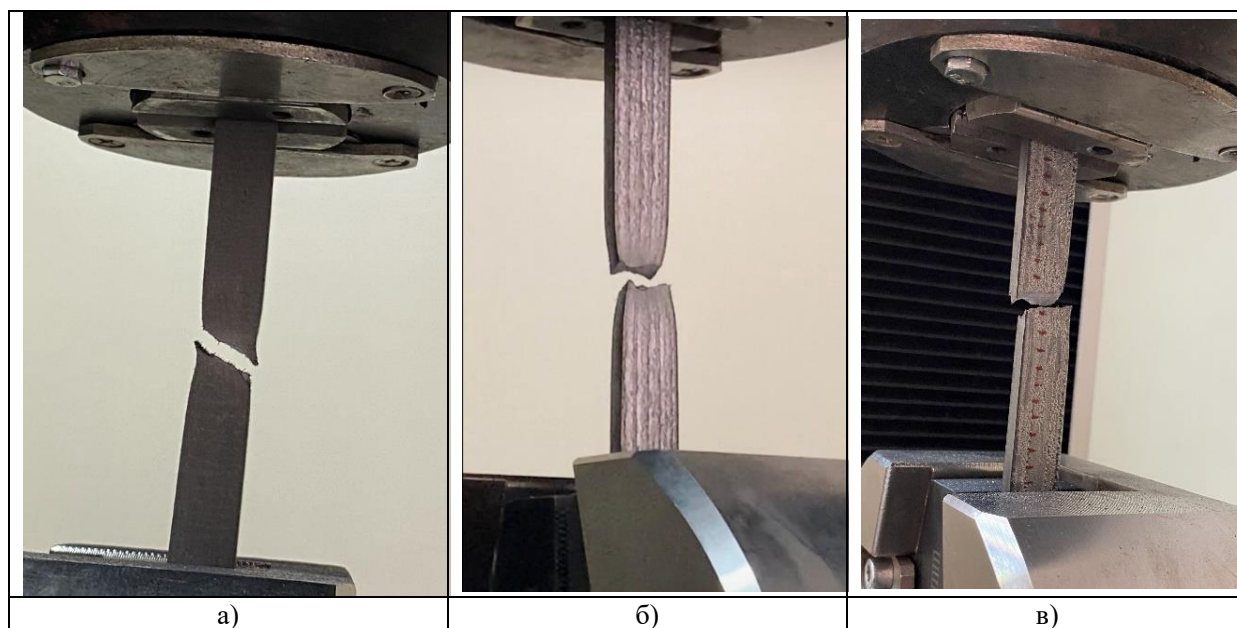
Испытания образцов материала на растяжение: а – необработанный образец, б – образец, закаленный лазером, в – образец, легированный лазером
